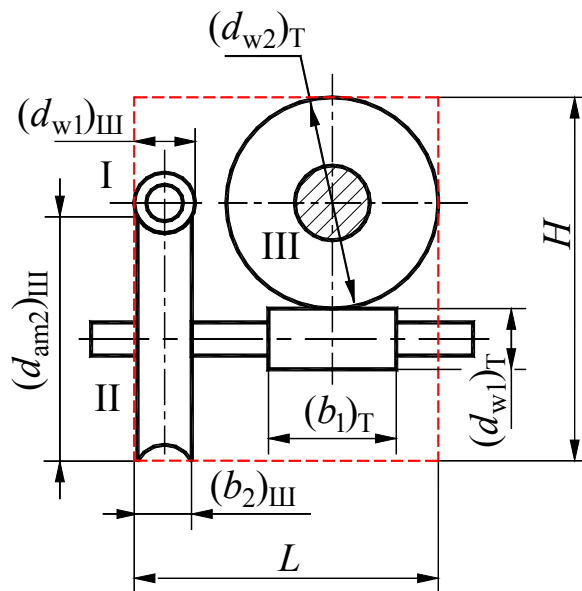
Черв'ячний двоступінчастий редуктор
